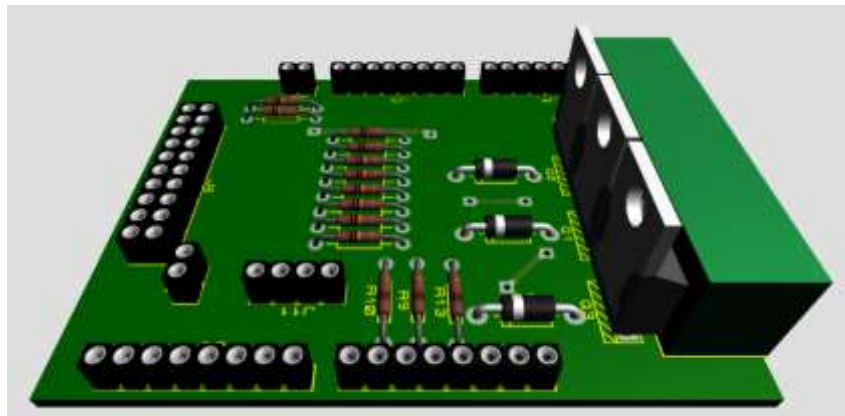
Diseño de la Shield en Proteus que irá Montada sobre la Tarjeta Arduino Mega
